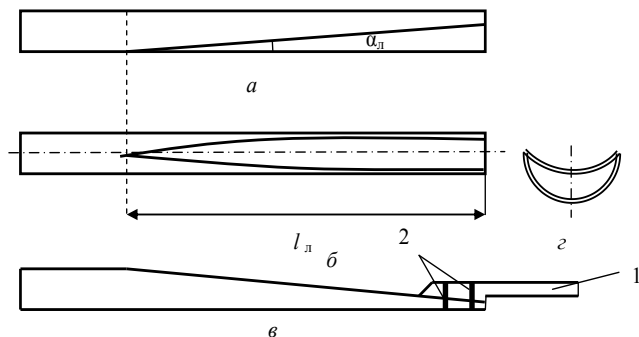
Схемы, поясняющие процесс изготовления стационарного клина: а, б – разметка линия отреза, при изготовлении ложка; в – схема клина с установочным патрубком 1 и срезными штифтами 2; з – поперечное сечение ложка клина
